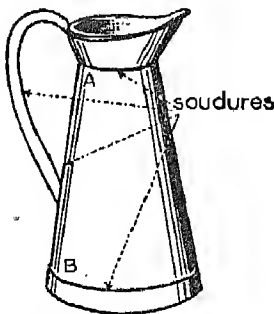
Ce broc en zinc comporte de nombreuses soudures.
